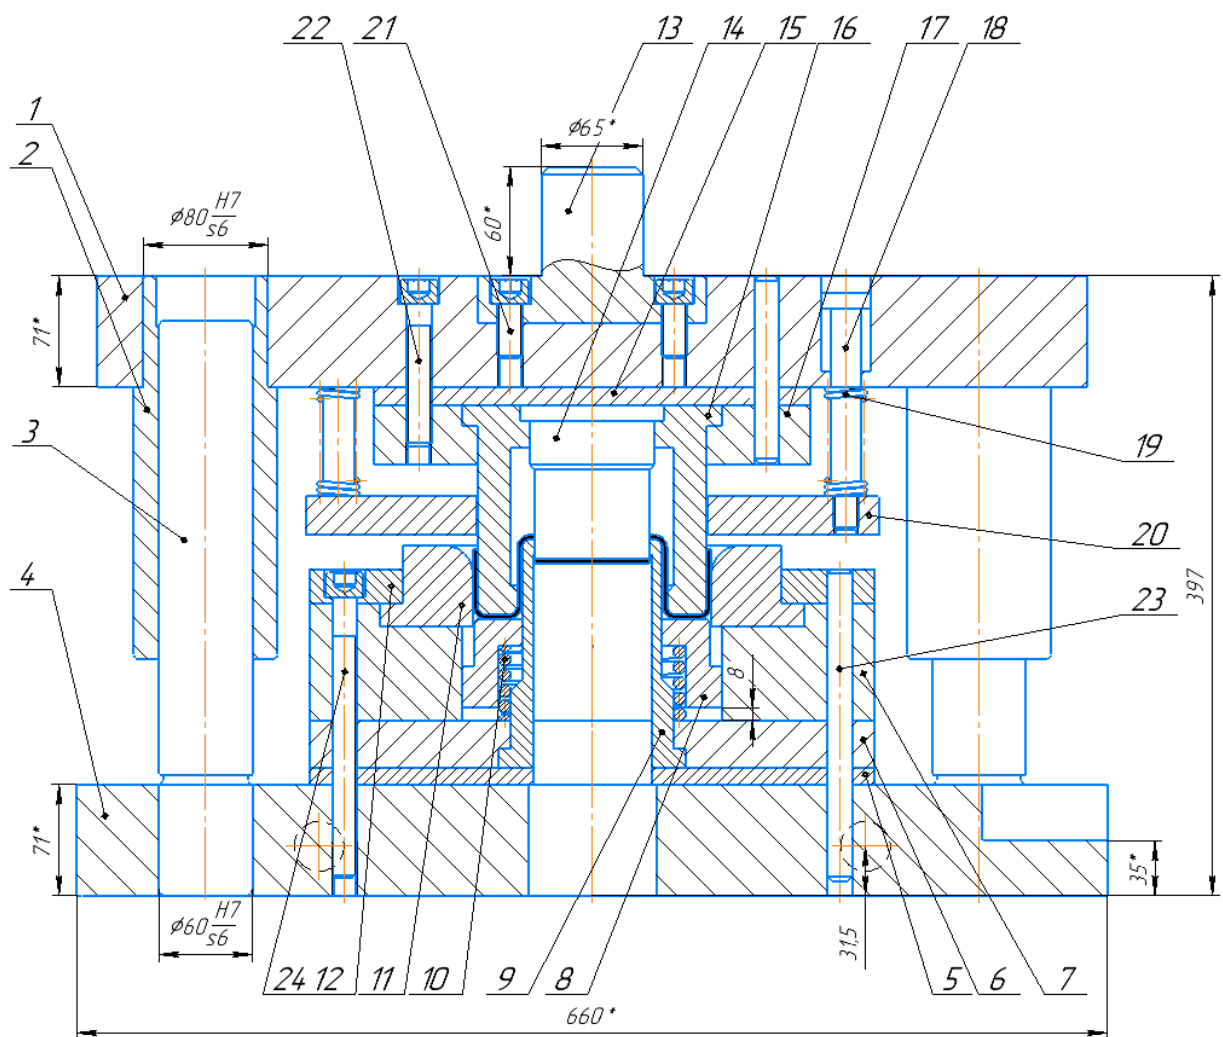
Общий вид штампа для калибровки-пробивки:
